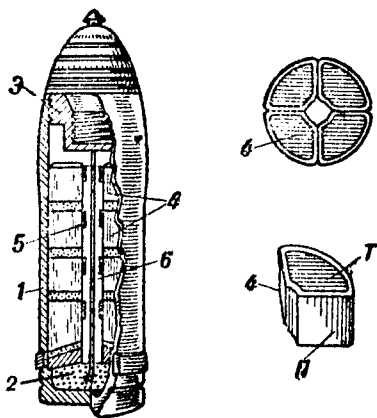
Зажигательный снаряд. 1 — корпус снаряда; 2 — вышибной заряд (дымный порох); 3 — головка с ввернутой в нее дистанционной трубкой; 4 — зажигательные термитные сегменты; 5 и 6 — стопин; 7 — оболочка сегмента; Т — термит.
